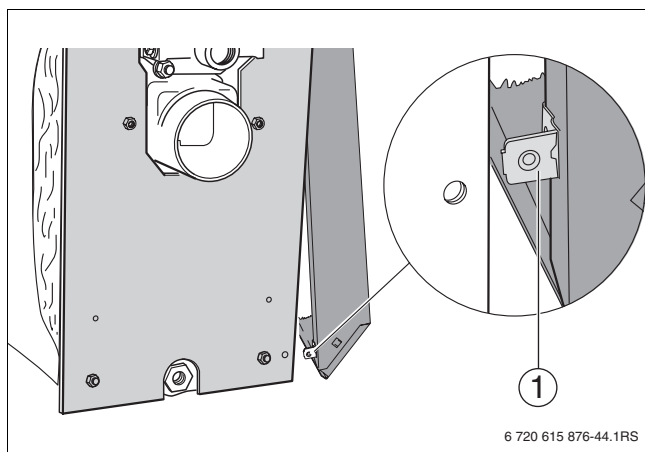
Fixer la paroi latérale avec la paroi arrière
